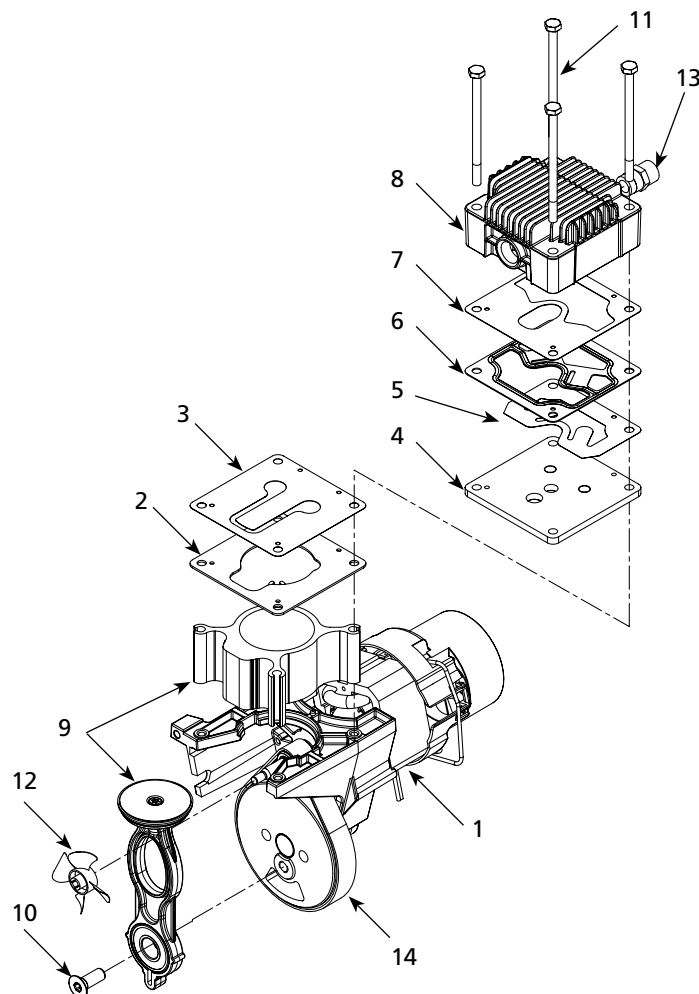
Illustration des pièces de rechange de la pompe, modèle WL390100
